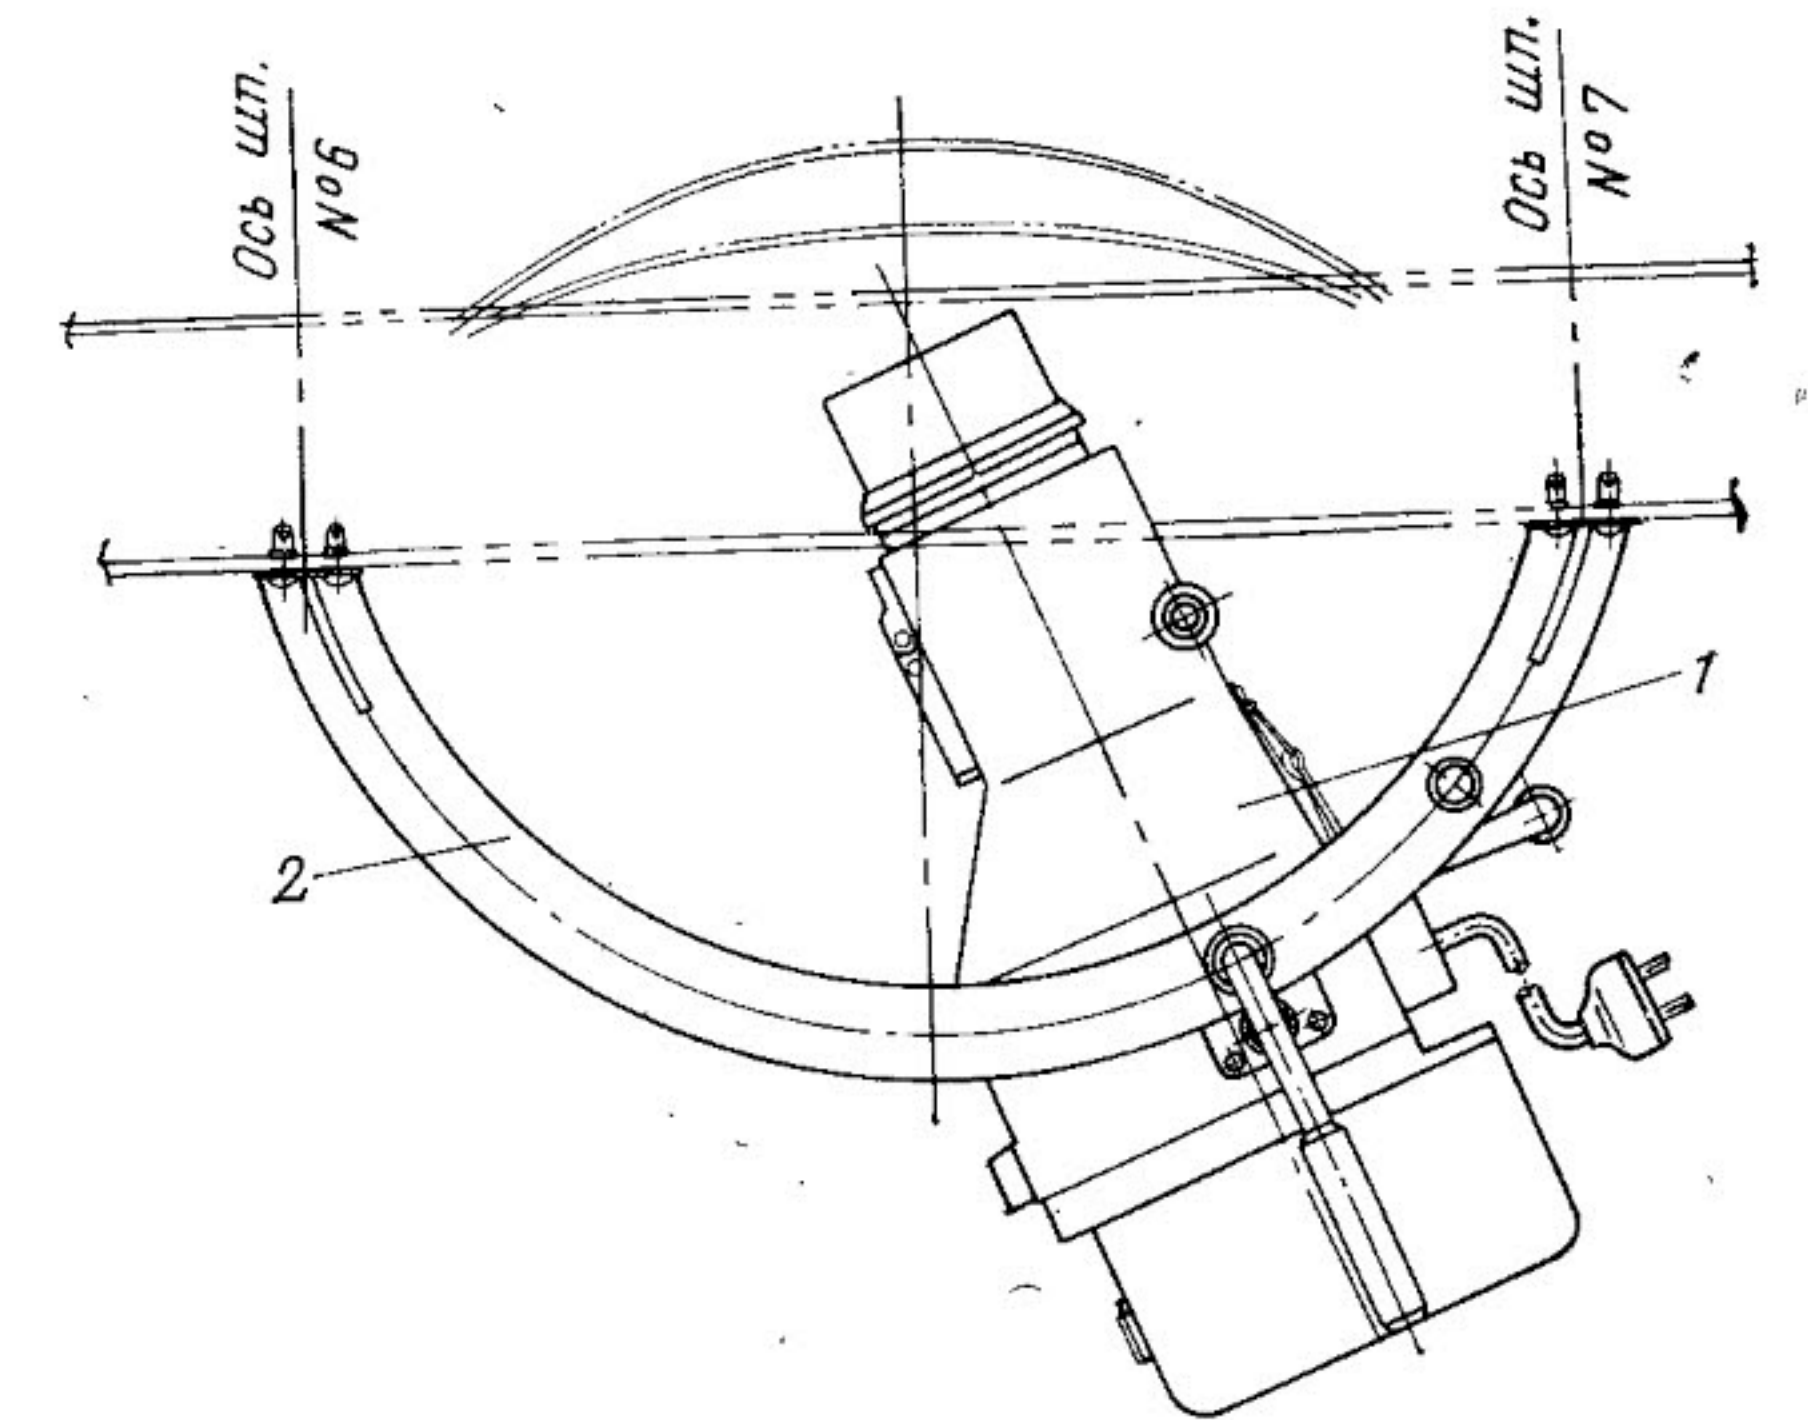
Установка фотокамеры для проверки соконусности лопастей несущего винта:
